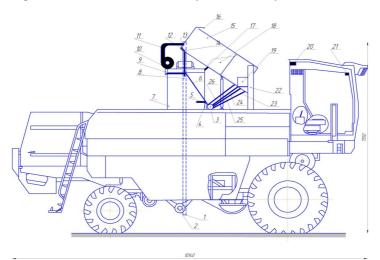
Конструктивная компоновка зерноуборочного комбайна Енисей 1200
